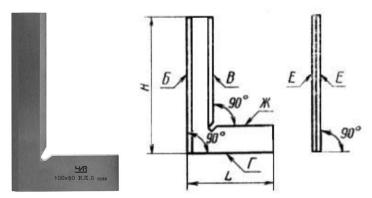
Общий вид угольников УЛП, обозначение основных размеров и поверхностей
